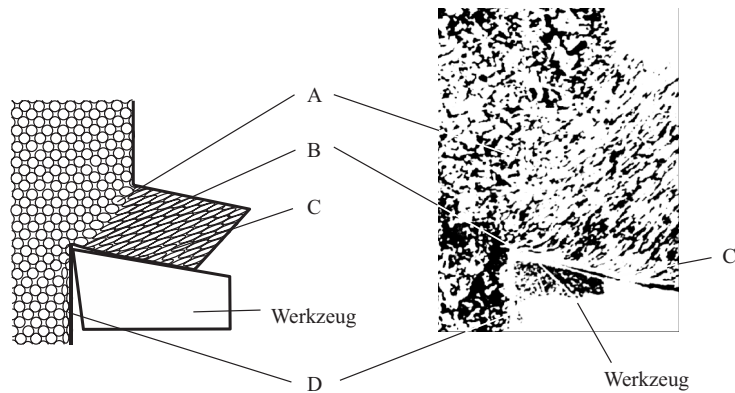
Spanbildung und Spanstruktur (nach [5])
